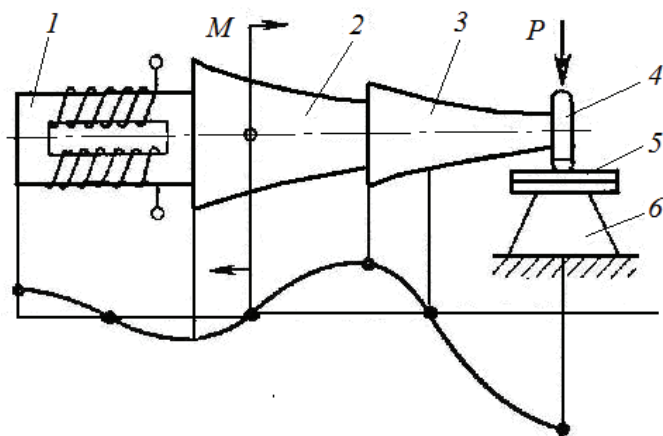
Принципиальная схема ультразвуковой сварки:
